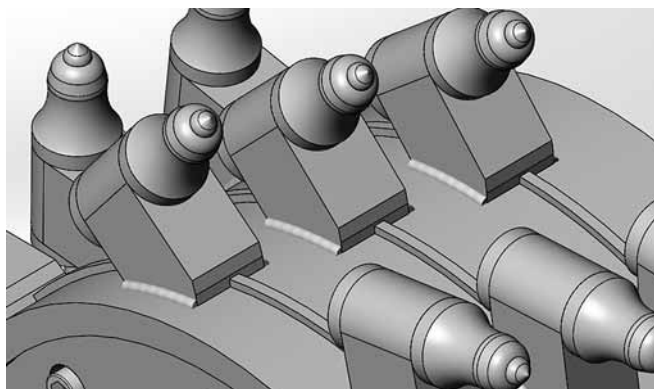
Сварное соединение резцедержатель—барабан
